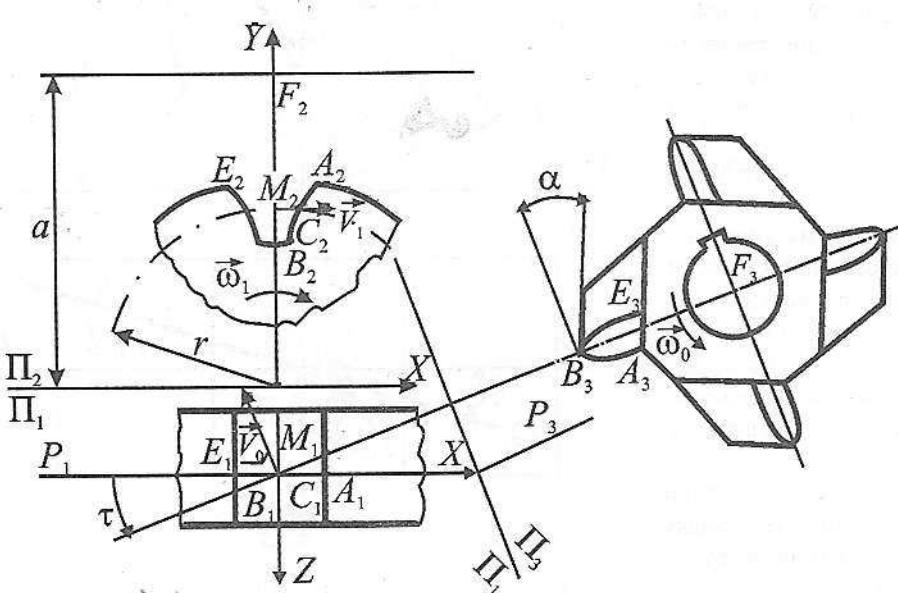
Схема приближенного профилирования обкаточной фрезы
